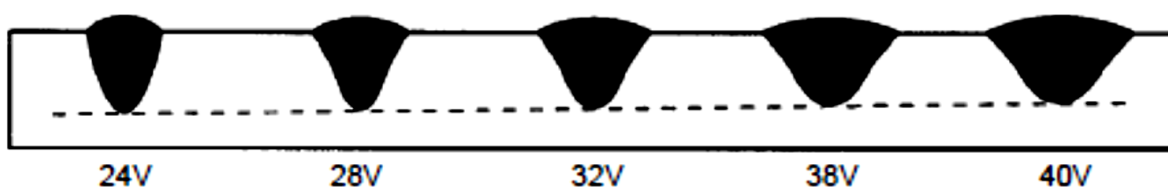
Efecto del voltaje en una soldadura [23].
